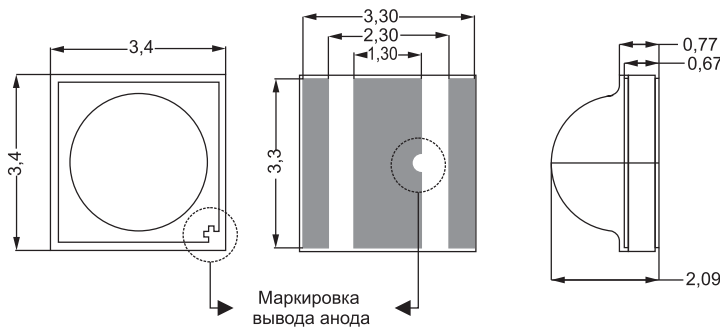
Габаритный чертеж приборов группы LEMWA33
